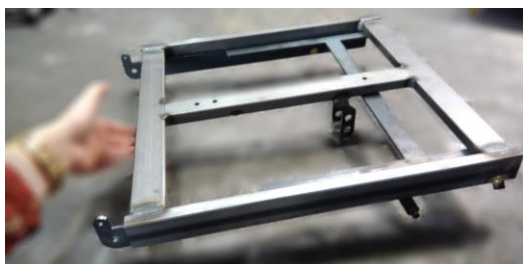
Estrutura soldada, representativa de parte do assento
